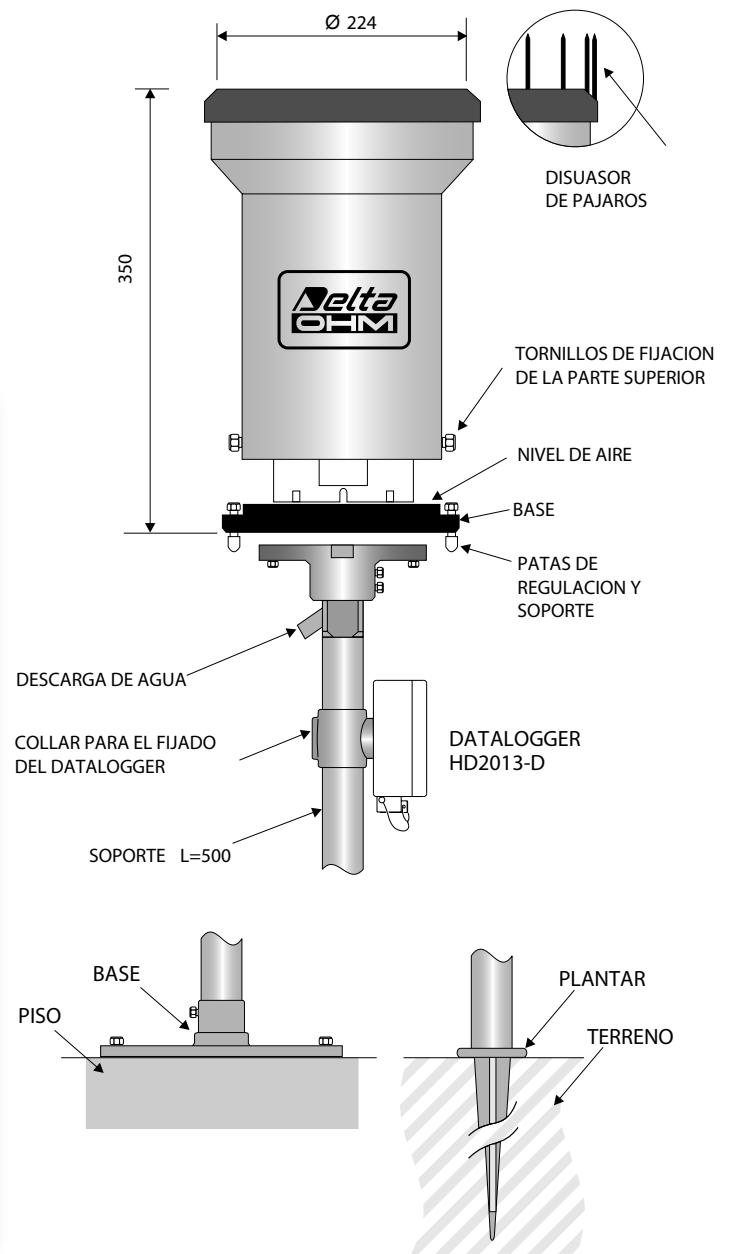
Dimensiones mecánicas, sistemas de instalación.
